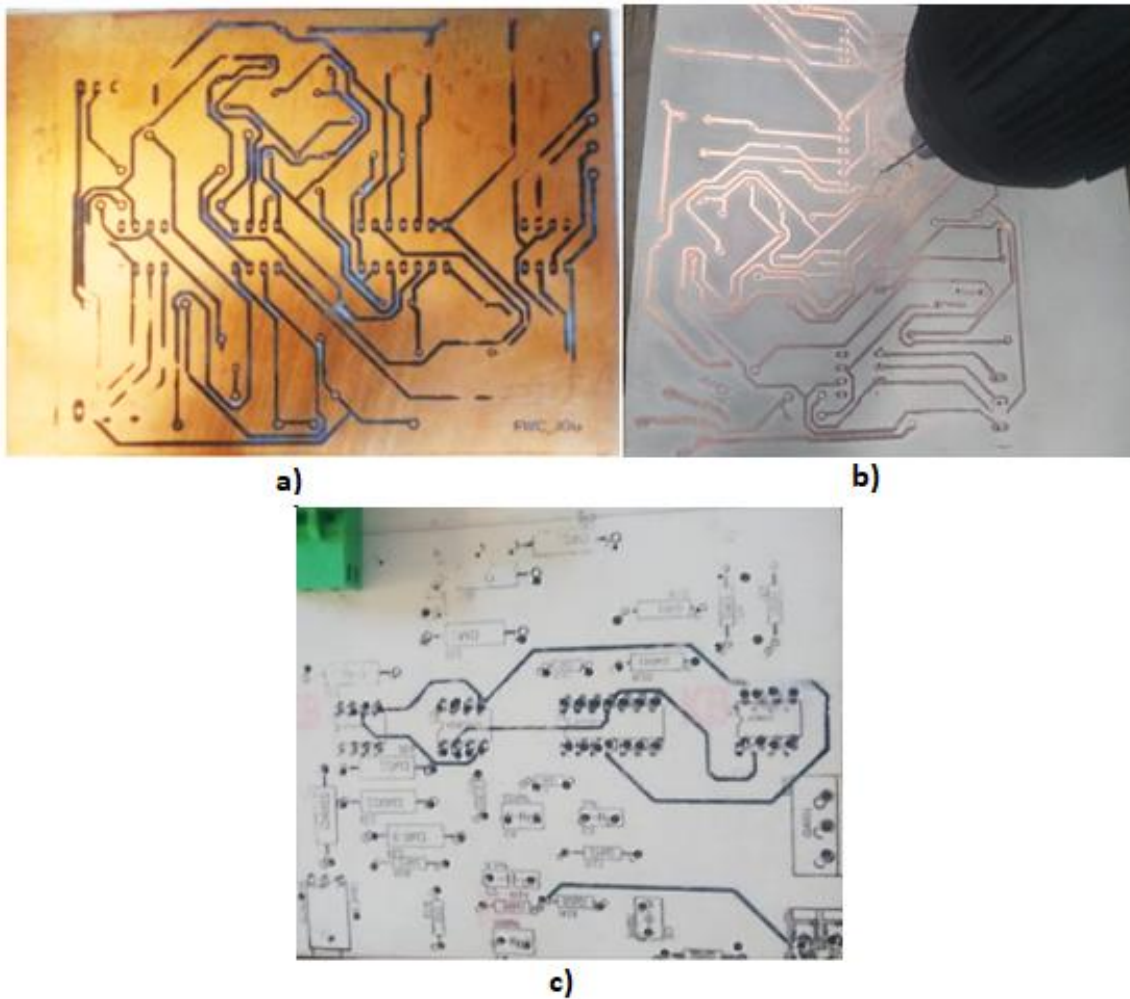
Muestra de las tarjetas de PCB, a) marcado de pistas sobre placa, b) placa después del proceso químico para la remoción del exceso de cobre y c) placa con perforaciones para colocar componentes.
